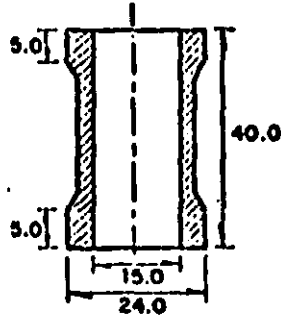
Dispositivo de carga axial, cámara T-3.6-60 (Ref 10)
